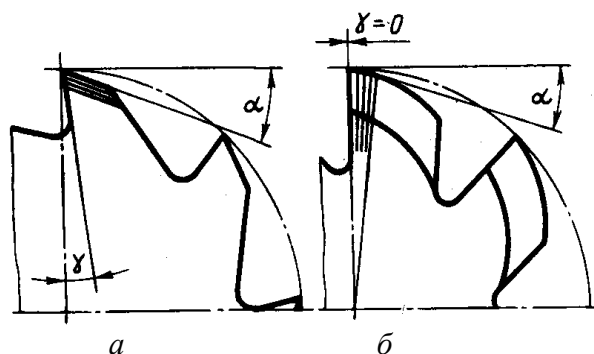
Схема заточки фрез: а – острозаточенных; б – затылованных
